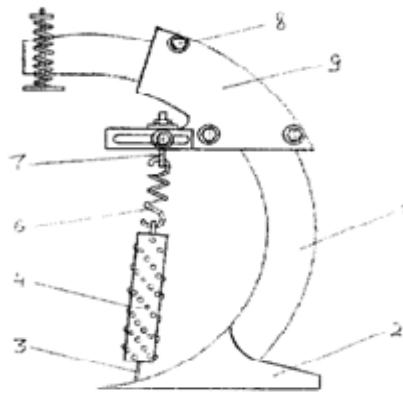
Робочий орган з елементами вібрації: 1 – стійка; 2 – розпушувальна лапа; 3 – гнучкий елемент типу струни; 4 – шипи; 6 – пружина; 7 – регулювальний гвинт; 8 – стяжний болт; 9 – кронштейн.
